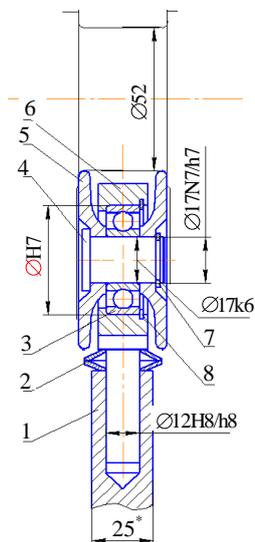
Ролик для ППД галтелей коленчатого вала:
